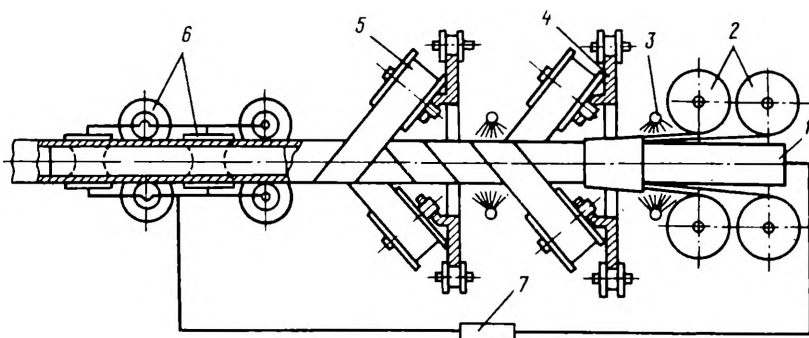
Схема горизонтальной установки для изготовления труб из стеклопластиков
